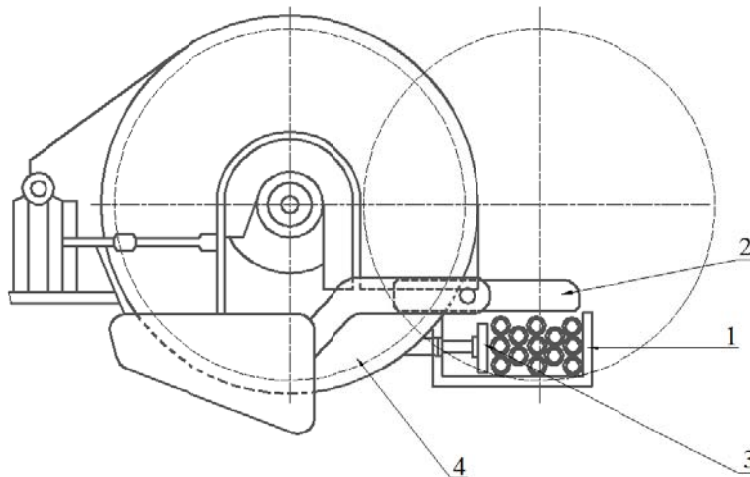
Укладка труб в лоток салазковой пилы пакетной резки холодного металлопроката в цехе ТПЦ – 2 АО «ВТЗ»
